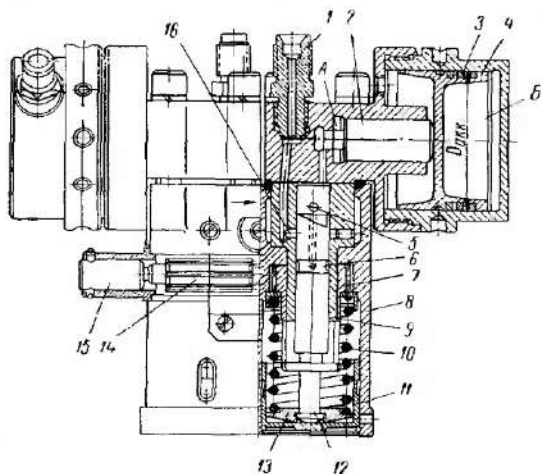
Топливный насос с пружинным приводом плунжера для дизель-компрессора:
